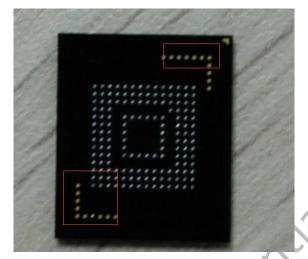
PCBA 焊盘定位脚和 flash 的测试点
